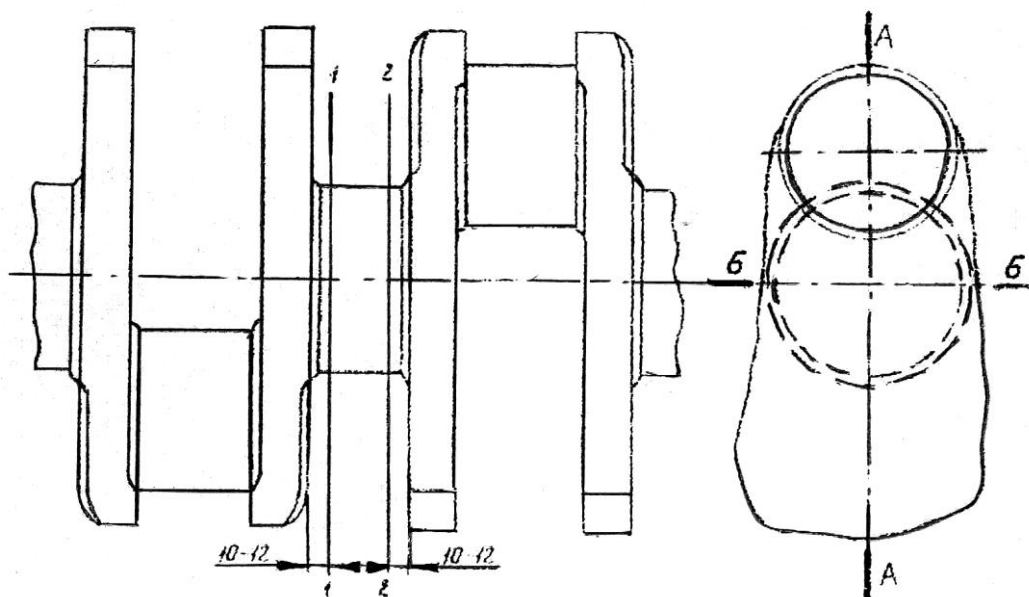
Схема направлений измерения диаметра коренных шеек коленчатого вала.
